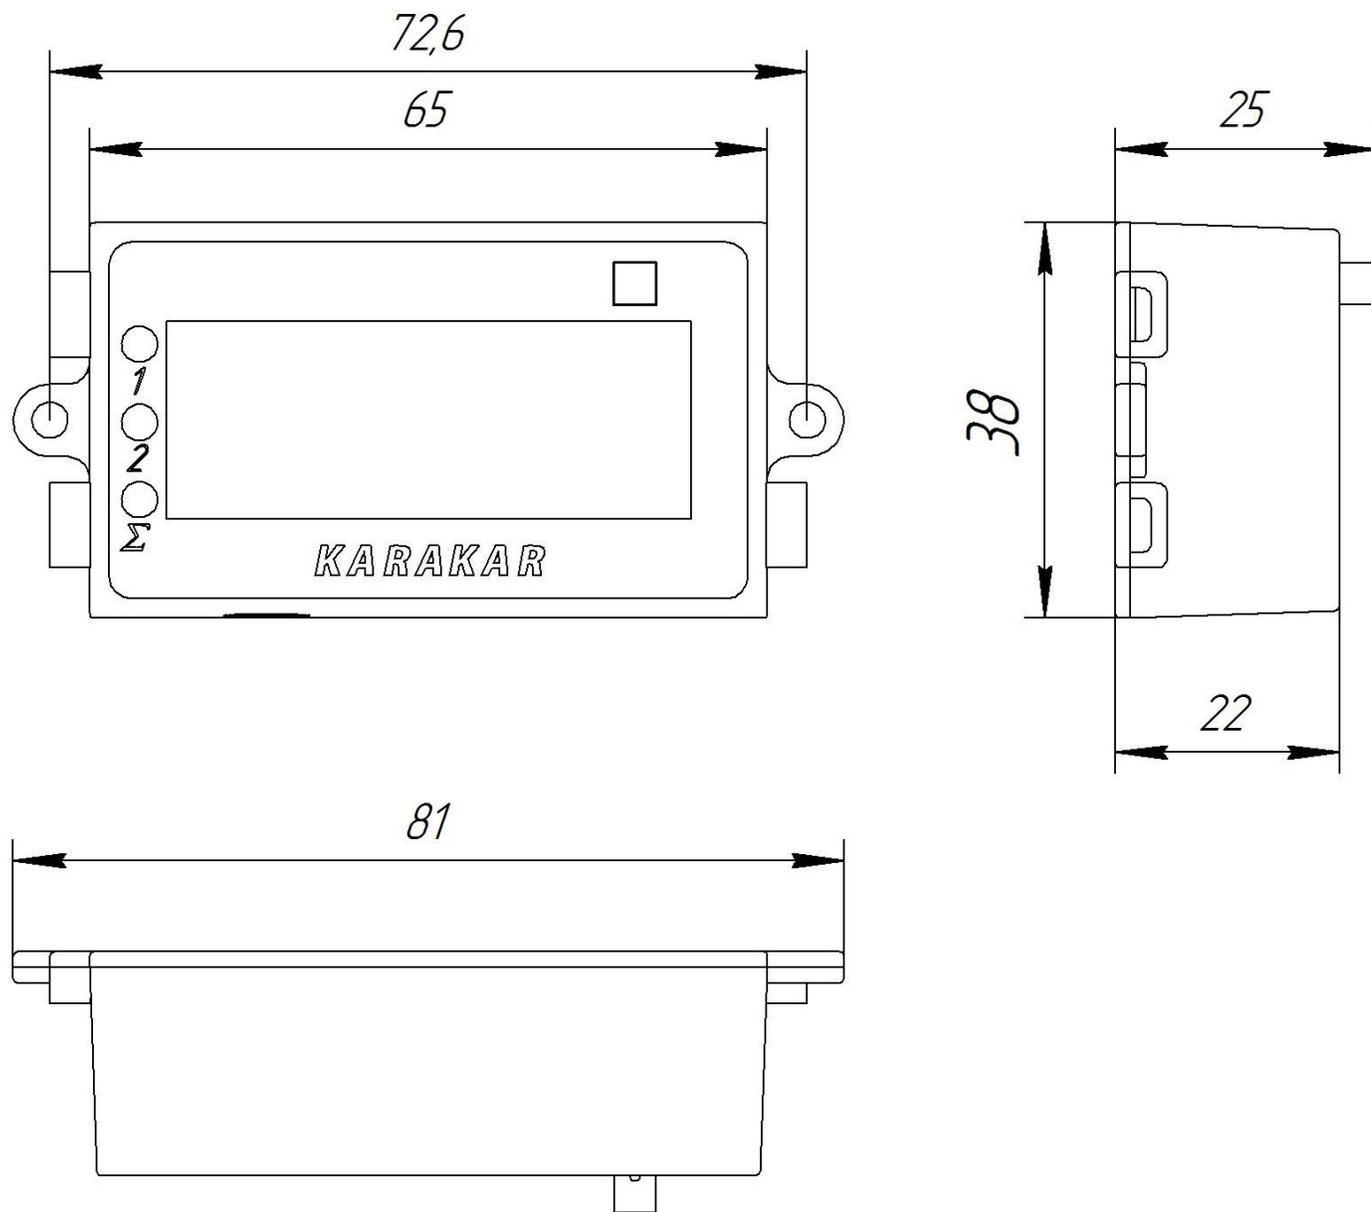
Габаритный чертеж индикатора объема топлива FLI
